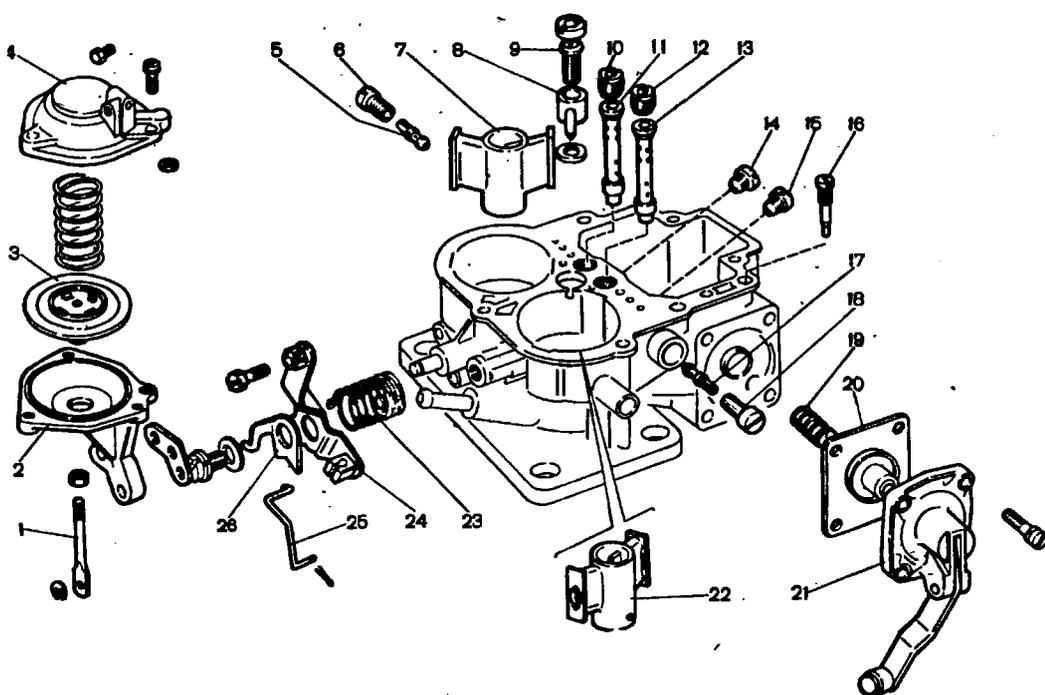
Детали корпуса карбюратора 2107-1107010: 1 - шток пневмопривода второй дроссельной заслонки; 2 - корпус пневмопривода; 3 - диафрагма; 4 - крышка пневмопривода; 5 - топливный жиклер переходной системы второй камеры; 6 - корпус топливного жиклера; 7 - малый диффузор второй камеры; 8 - распылитель ускорительного насоса; 9 - винт-клапан ускорительного насоса; 10 - главный воздушный жиклер второй камеры; 11 - эмульсионная трубка второй камеры; 12 - главный воздушный жиклер первой камеры; 13 - эмульсионная трубка первой камеры; 14 - главный топливный жиклер второй камеры; 15 - главный топливный жиклер первой камеры; 16 - регулировочный винт ускорительного насоса; 17 - топливный жиклер системы холостого хода; 18 - корпус топливного жиклера; 19 - возвратная пружина ускорительного насоса; 20 - диафрагма ускорительного насоса; 21 - крышка ускорительного насоса; 22 - малый диффузор первой камеры; 23 - возвратная пружина рычага; 24 - трехплечий рычаг управления воздушной заслонкой; 25 - тяга связи с дроссельной заслонкой; 26 - кронштейн возвратной пружины дроссельных заслонок
